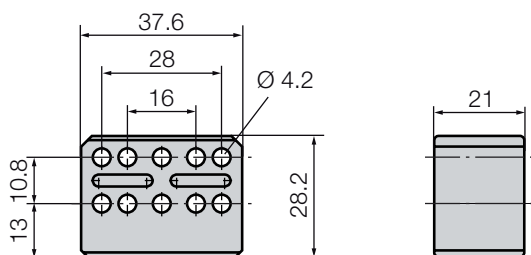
Medidas para montagem do encoder de posição BTL6-A-3800-2
